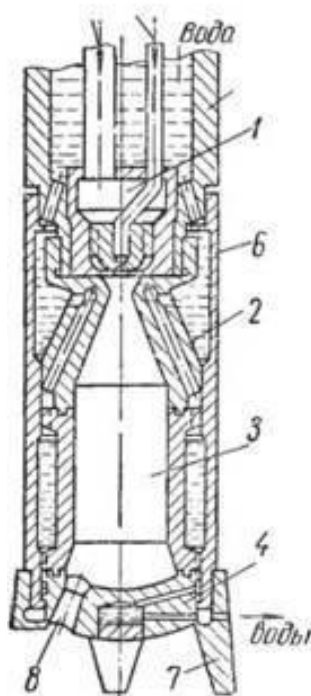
Схема трёхсопловой реактивной горелки: 1 – форсунка; 2 – корпус горелки; 3 – камера сгорания; 4 – головка горелки; 5 – переходник; 6 – кожух; 7 – башмак; 8 – сопло
